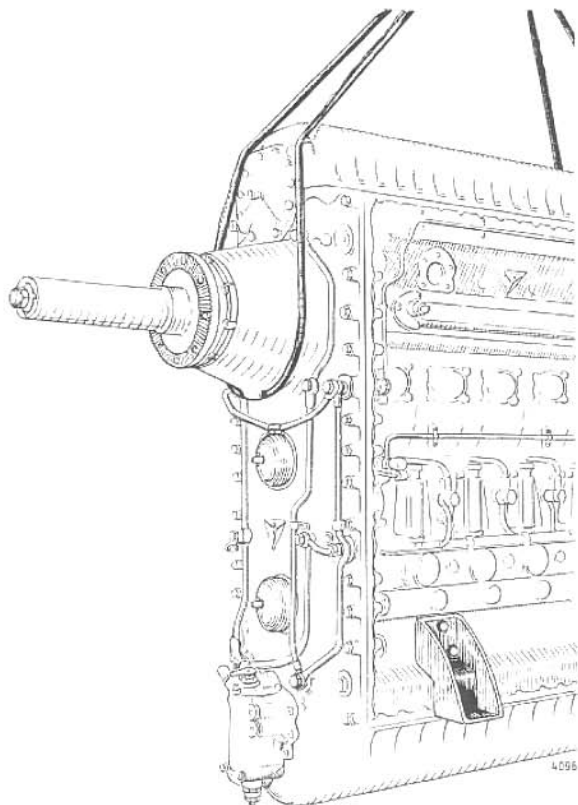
Anlegen des Krangehänges auf Luftschraubenseite
